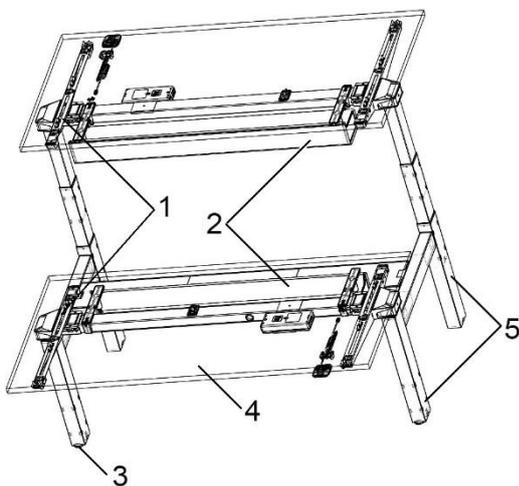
Ology Bench, variante elevador 1 y elevador 2
